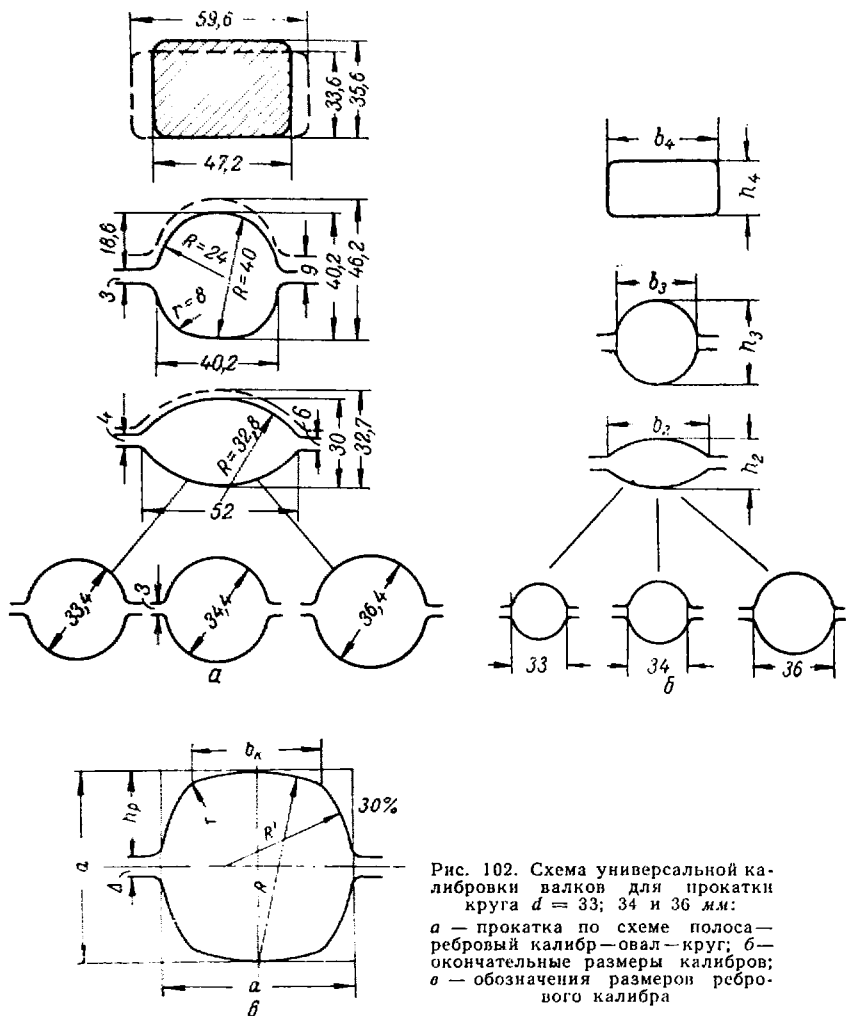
Схема универсальной калибровки валков для прокатки круга $d = 33; 34$ и 36 мм :
